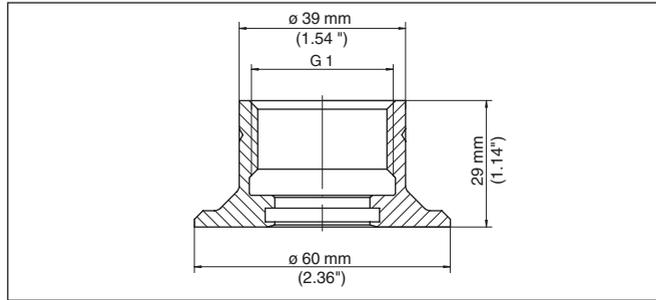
Dimensions raccord à souder G1 (DIN 3852-X)
